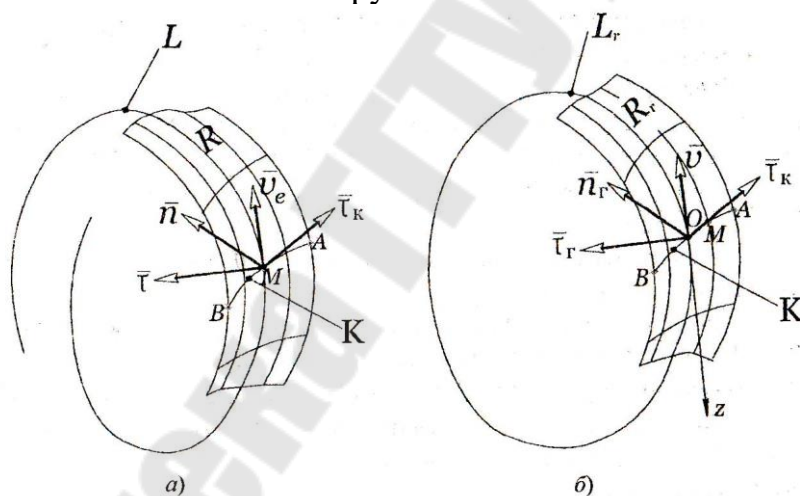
Схема формирования поверхности резания (а) и поверхности главного движения (б), а также расположения связанных с ними направляющих векторов
